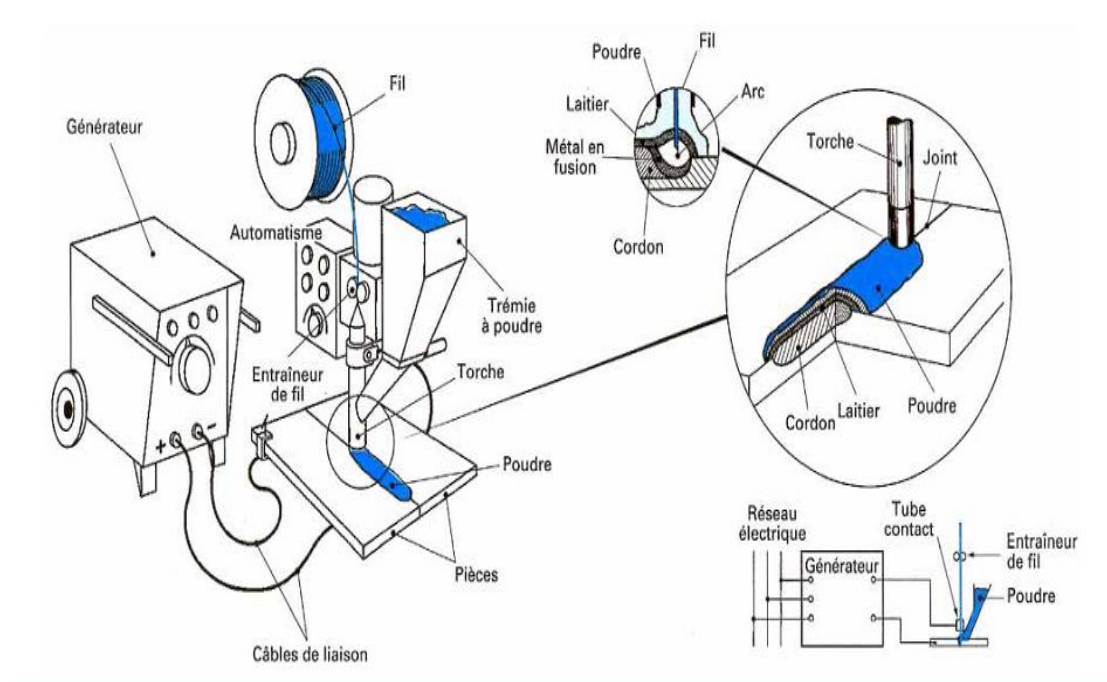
Soudage sous flux en poudre[11]
